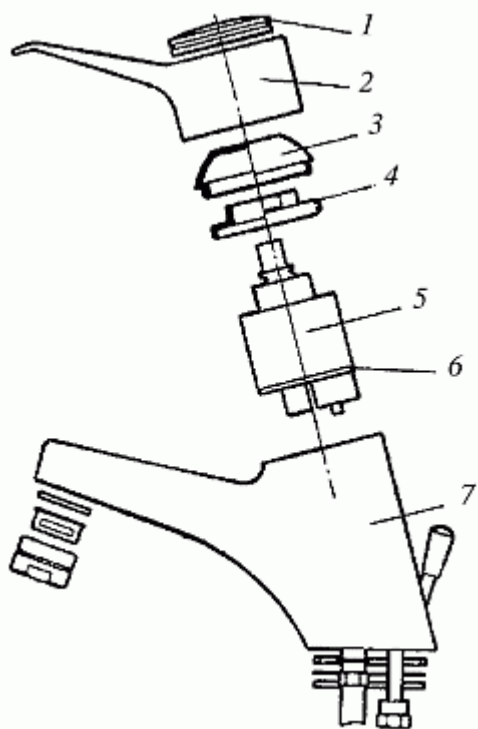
Устройство современного смесителя с аэратором и встроенным фильтром: 1 – фиксирующий элемент; 2 – поворотная рукоятка (джойстик); 3 – крышка корпуса; 4 – круговая гайка; 5 – сменный картридж механической очистки; 6 – прокладка; 7 – корпус
